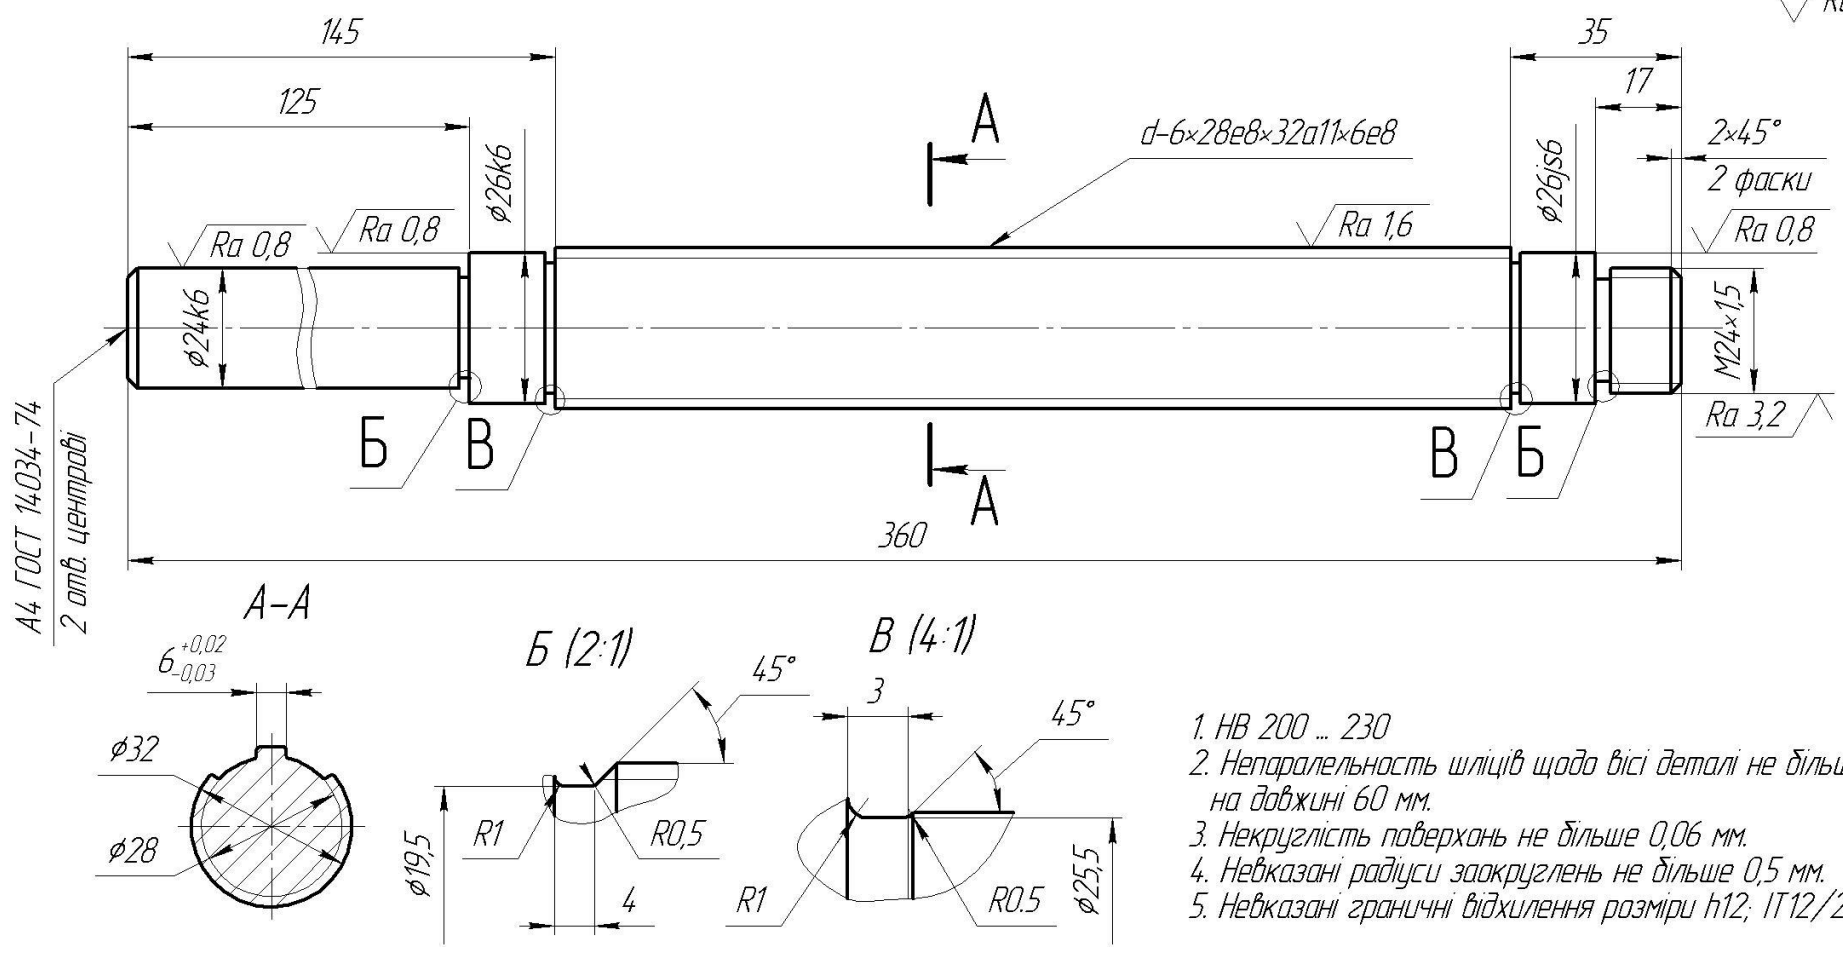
Кресленник деталі «Вал шліцьовий»
